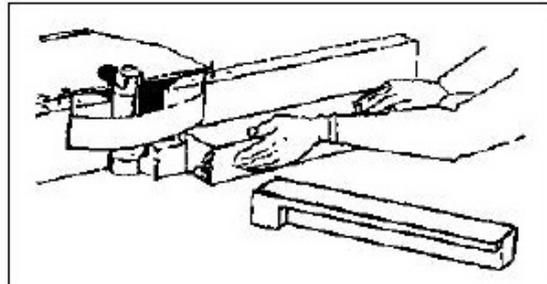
Bearbeitung von Werkstücken mit kleinem Querschnitt
